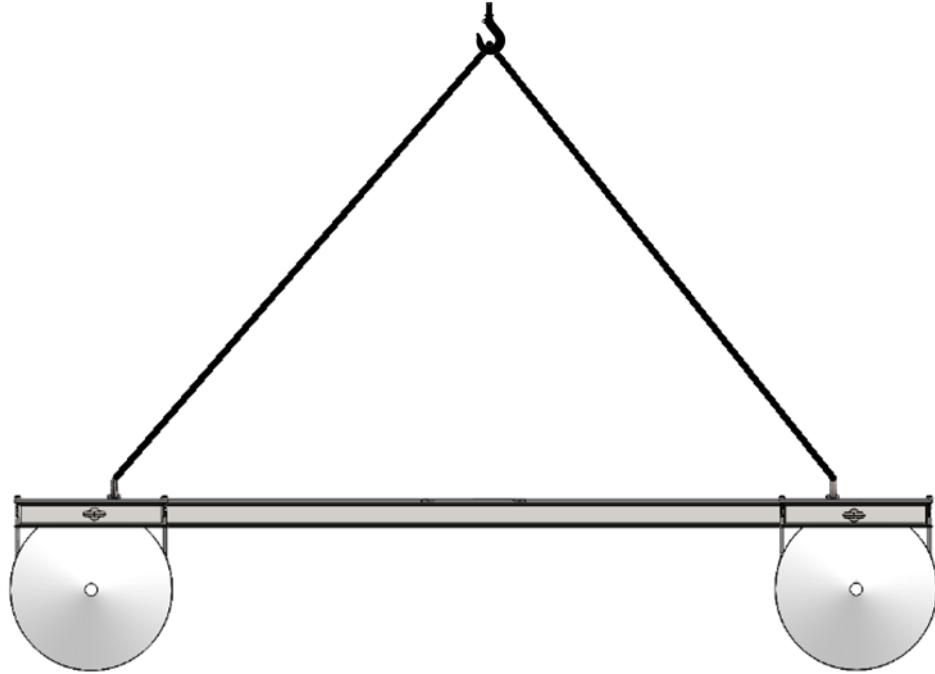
Vista frontal de elevación de sistema emplazamiento. Elaborado por los autores.
